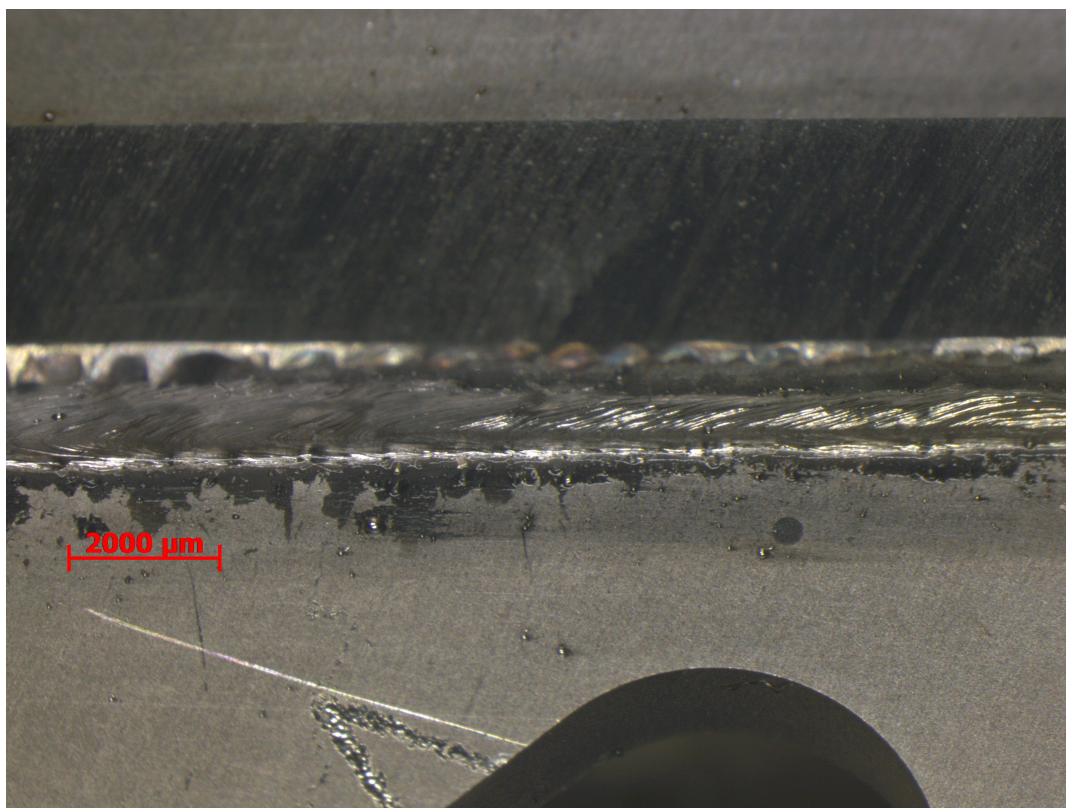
Vue macroscopique de l'envers du cordon de soudure débouchant.
